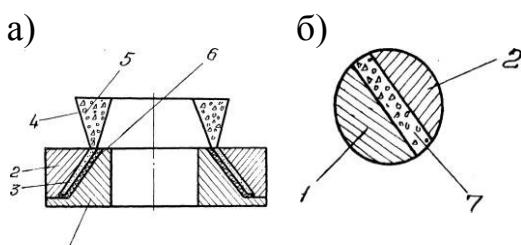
Розріз форми і деталі в зборі (а); зазор (б)
